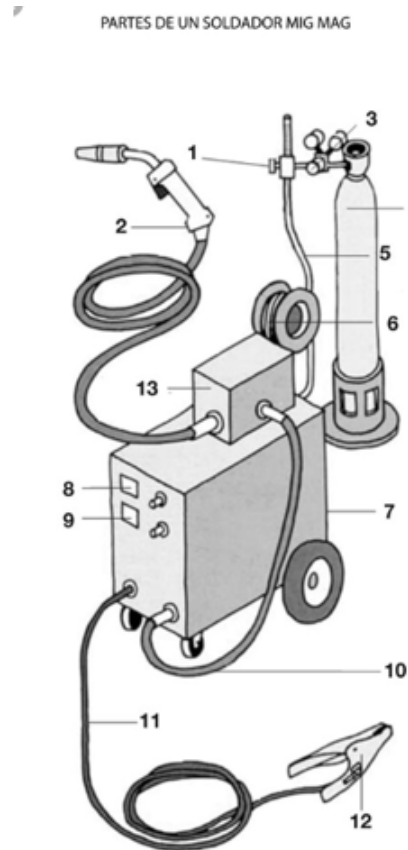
soldadora MIG/MAG. Fuente: <https://www.demaquinasyherramientas.com>
